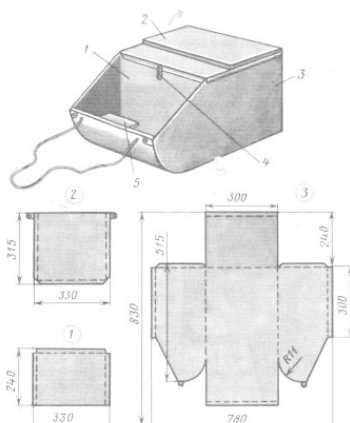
Самодельный ящик-санки конструкции Г. Балуева: 1 – передняя стенка (те же размеры и форма у внутренней перегородки), 2 – крышка ящика с сиденьем из пенопласта, 3 – корпус из листового дюрала; 4 – защелка-затвор; 5 – ручка-полка из семислойной фанеры.
